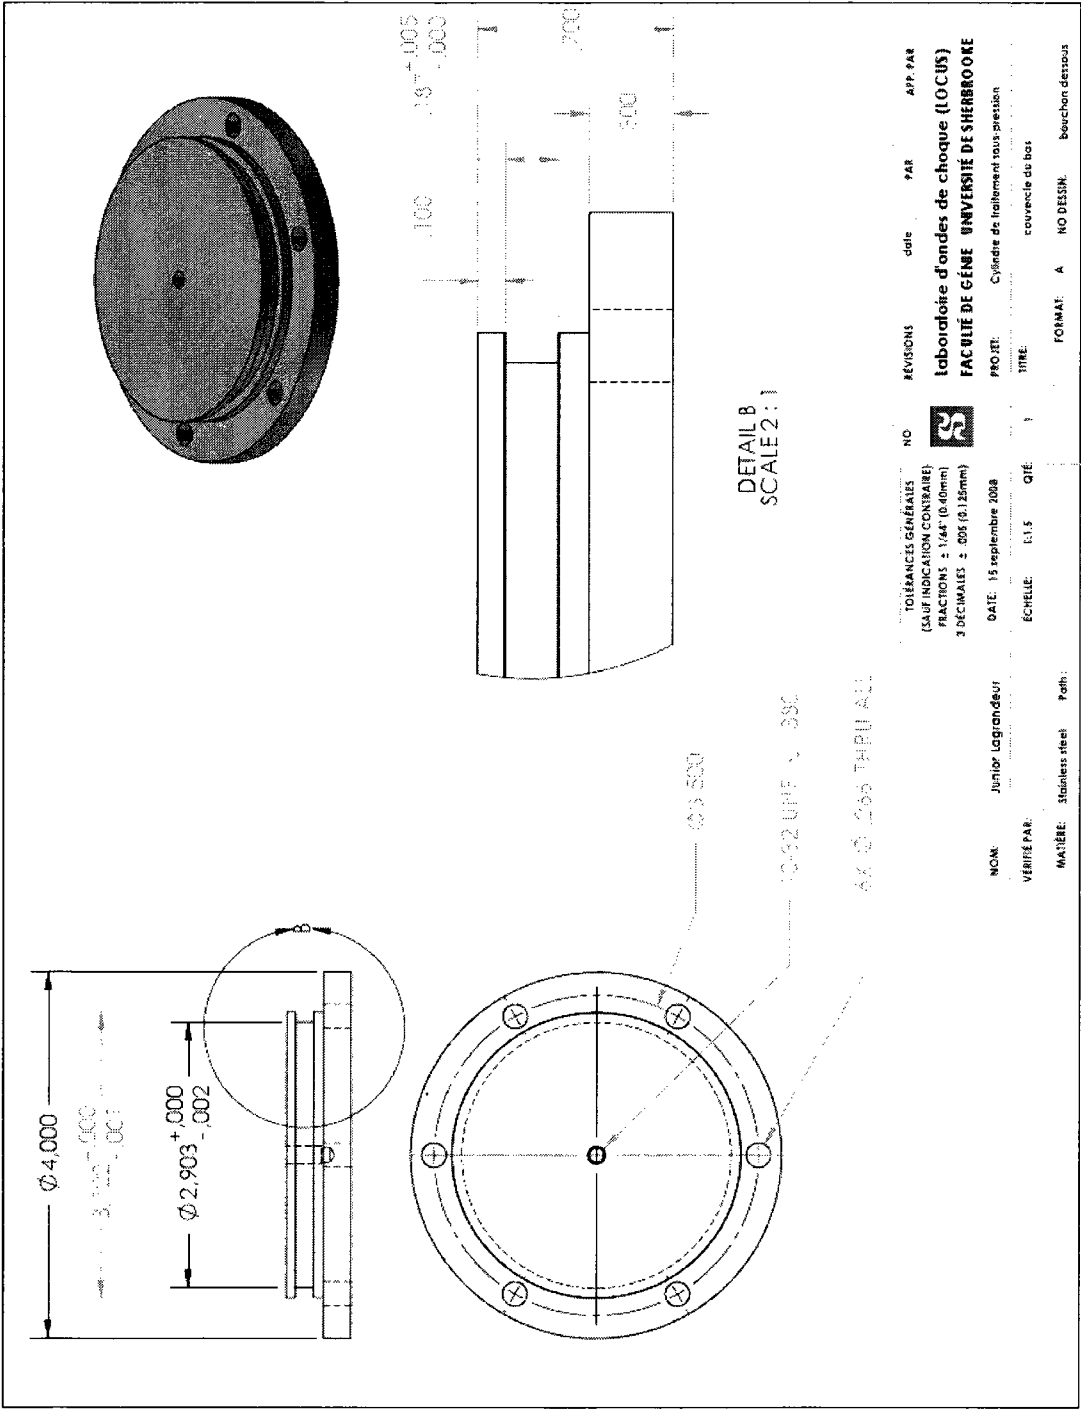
Dessin de fabrication du couvercle du bas du cylindre
